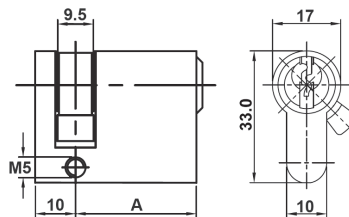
Dimensions de la serrure cylindrique en mm
